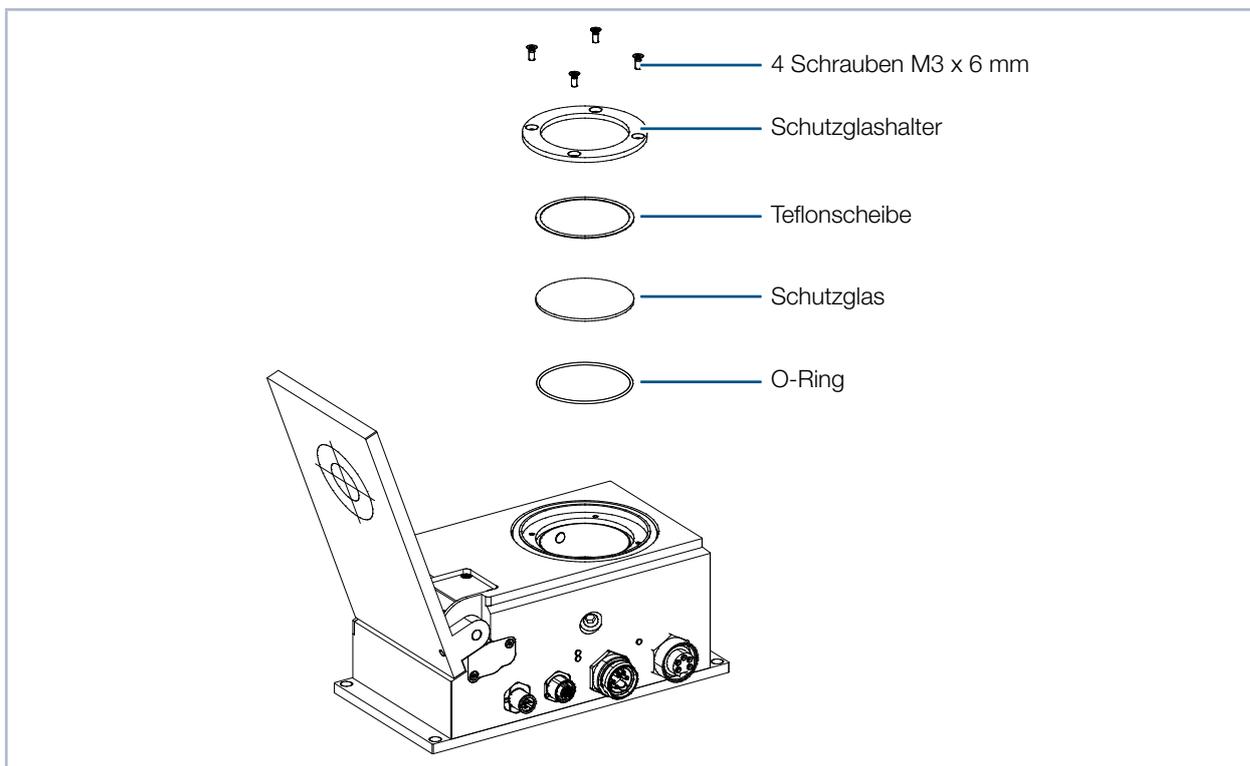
Explosionsdarstellung Schutzglasbefestigung
